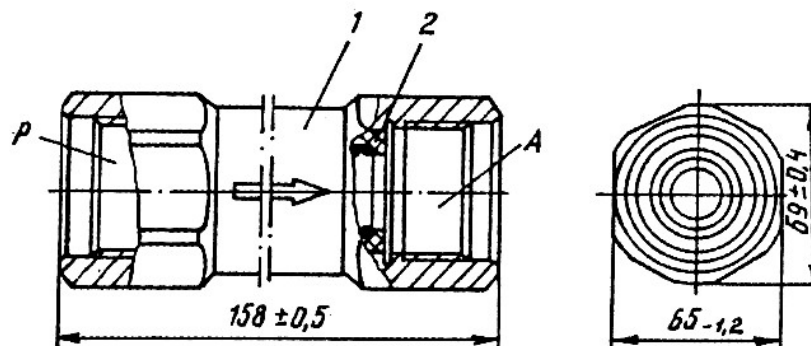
Общий вид обратного клапана типа 531.20.00
